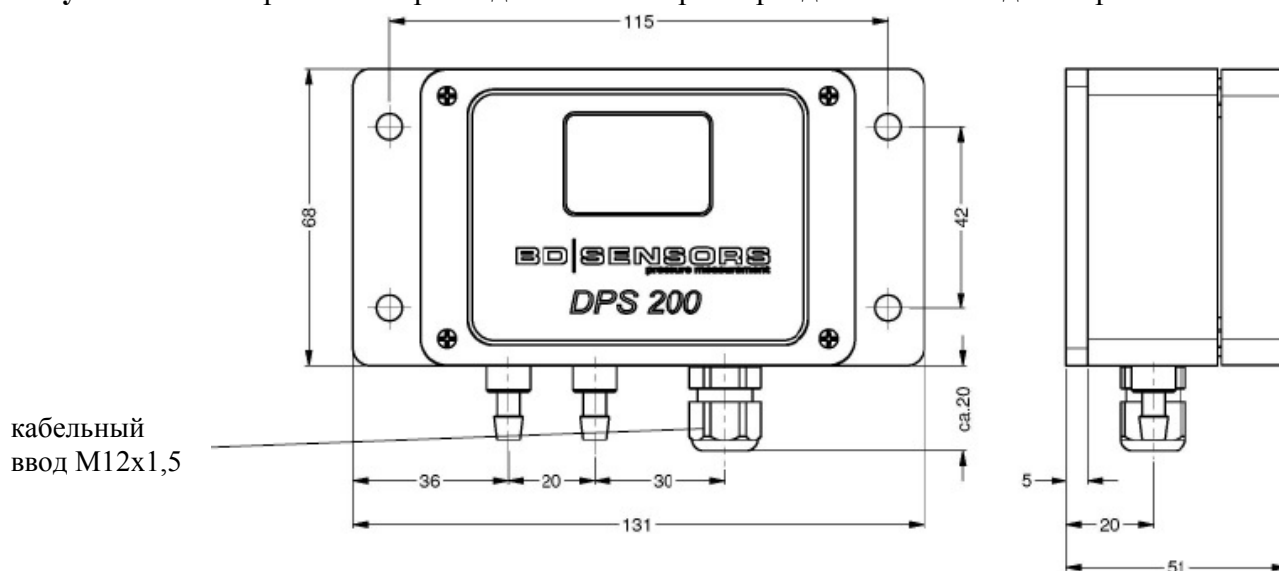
Габаритные и присоединительные размеры датчика с ЖК-индикатором.
